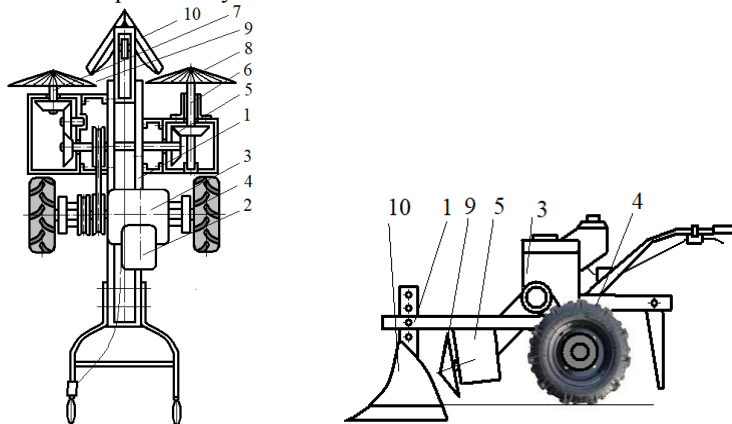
Пожарный грунтомет: 1-рама, 2-двигатель, 3-раздаточная коробка, 4-приводные колеса, 5-конический редуктор, 6, 7-выходные валы, 8, 9 – фрезы-метатели, 10 – плуг
